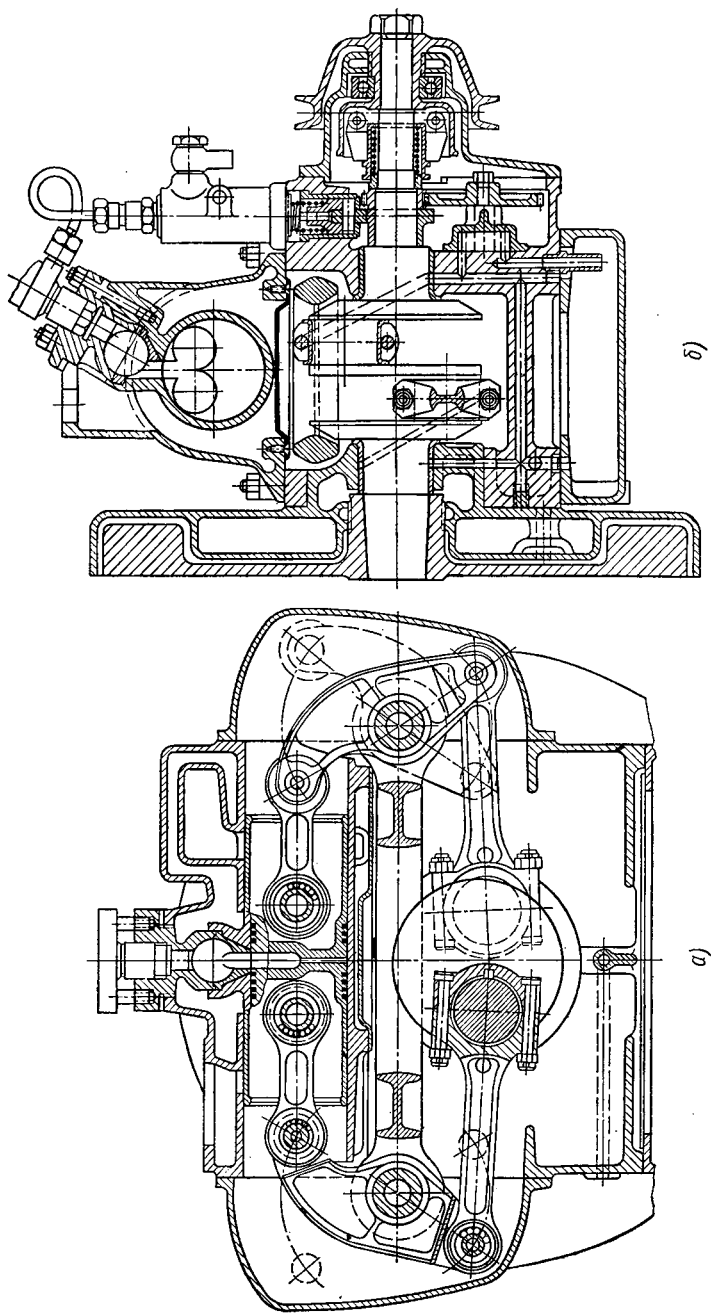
Двигатель с противоположно движущимися поршнями и передачей сил давления газов вала при помощи коромысел:
